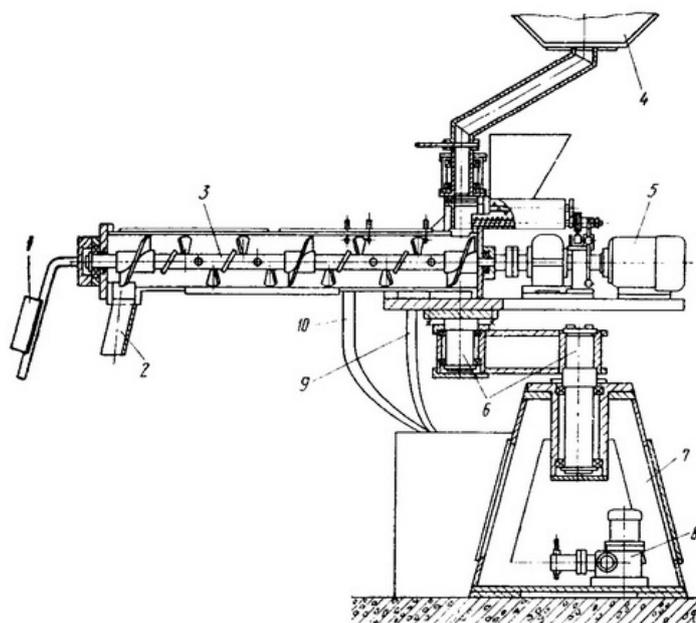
Общий вид установки ХТС для изготовления стержней [32]
